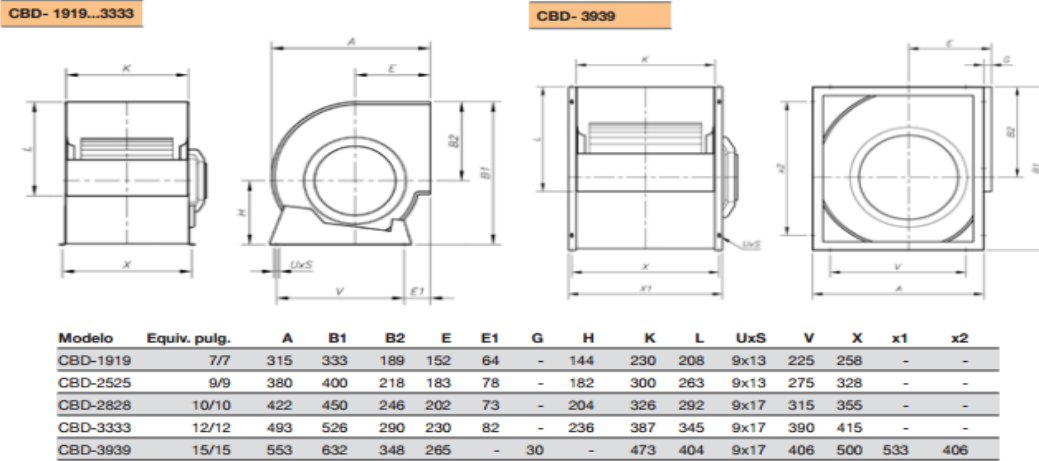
Dimensiones, Línea Sodeca CBD.
